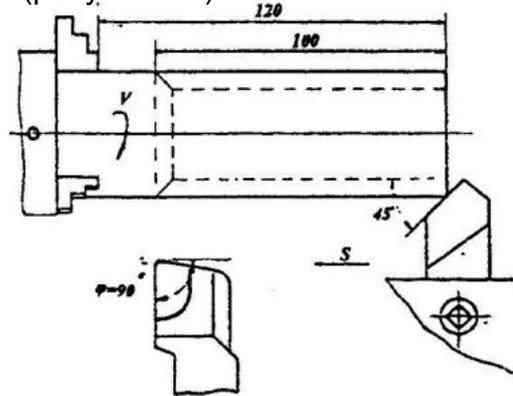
Консольное закрепление заготовки в трехкулачковом патроне
